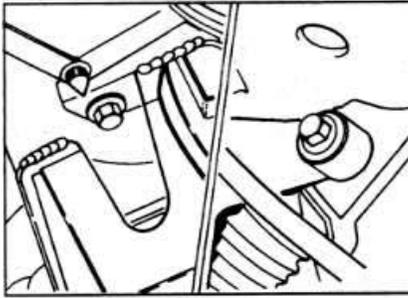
Расположение болта крепления подвески силового агрегата к поперечной балке.
